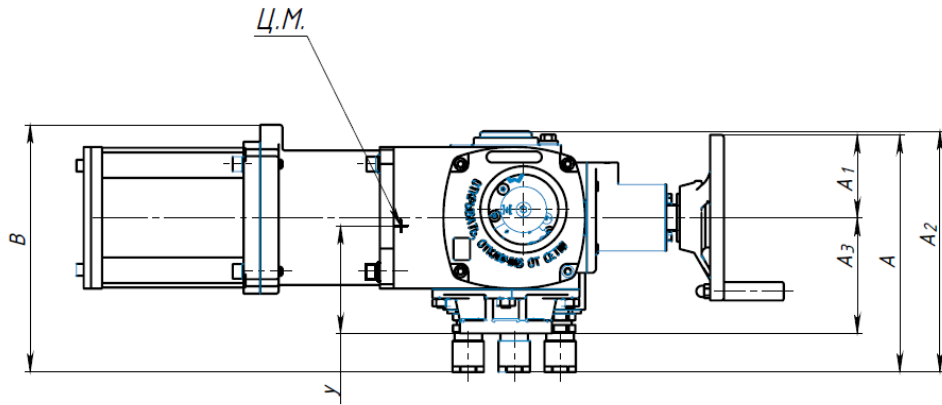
б – Габаритные размеры привода конструктивной схемы 41
